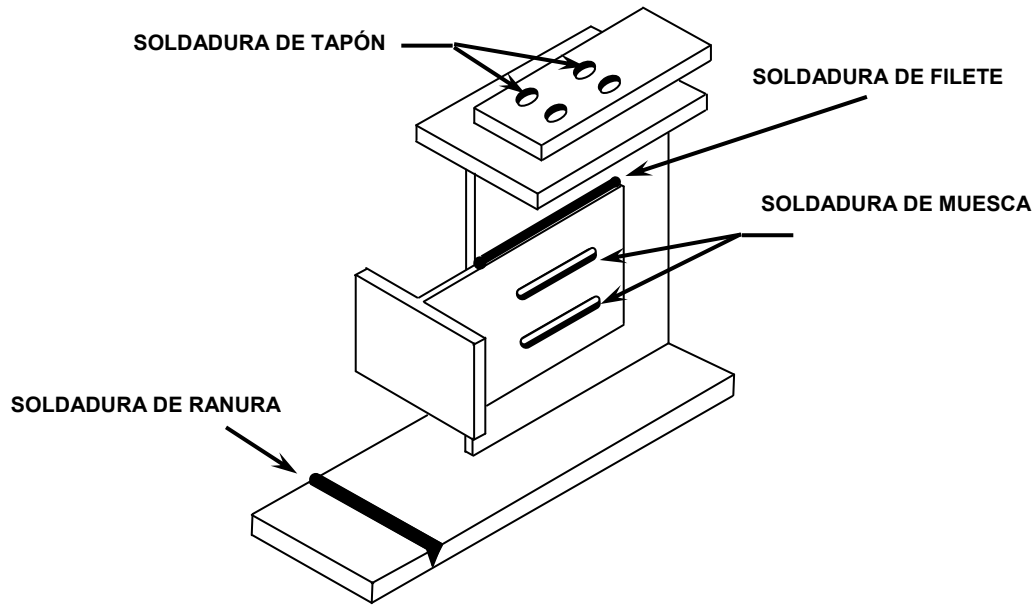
Soldaduras de filete, muesca, ranura y Tapón.
